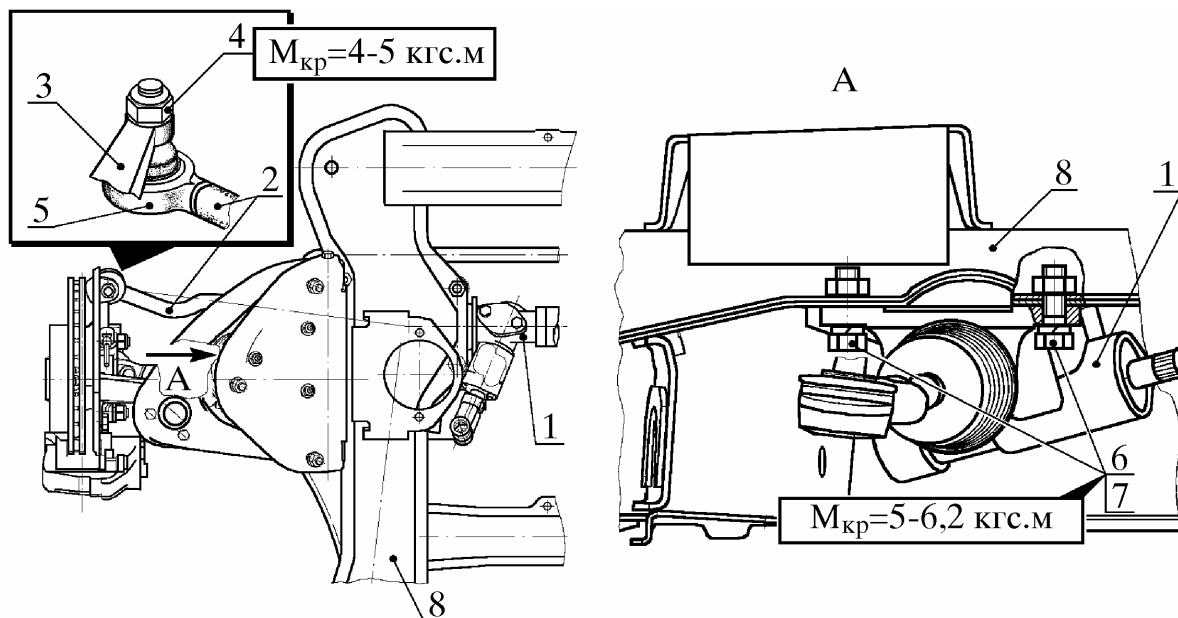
Установка рулевого механизма с рулевыми тягами в сборе:
